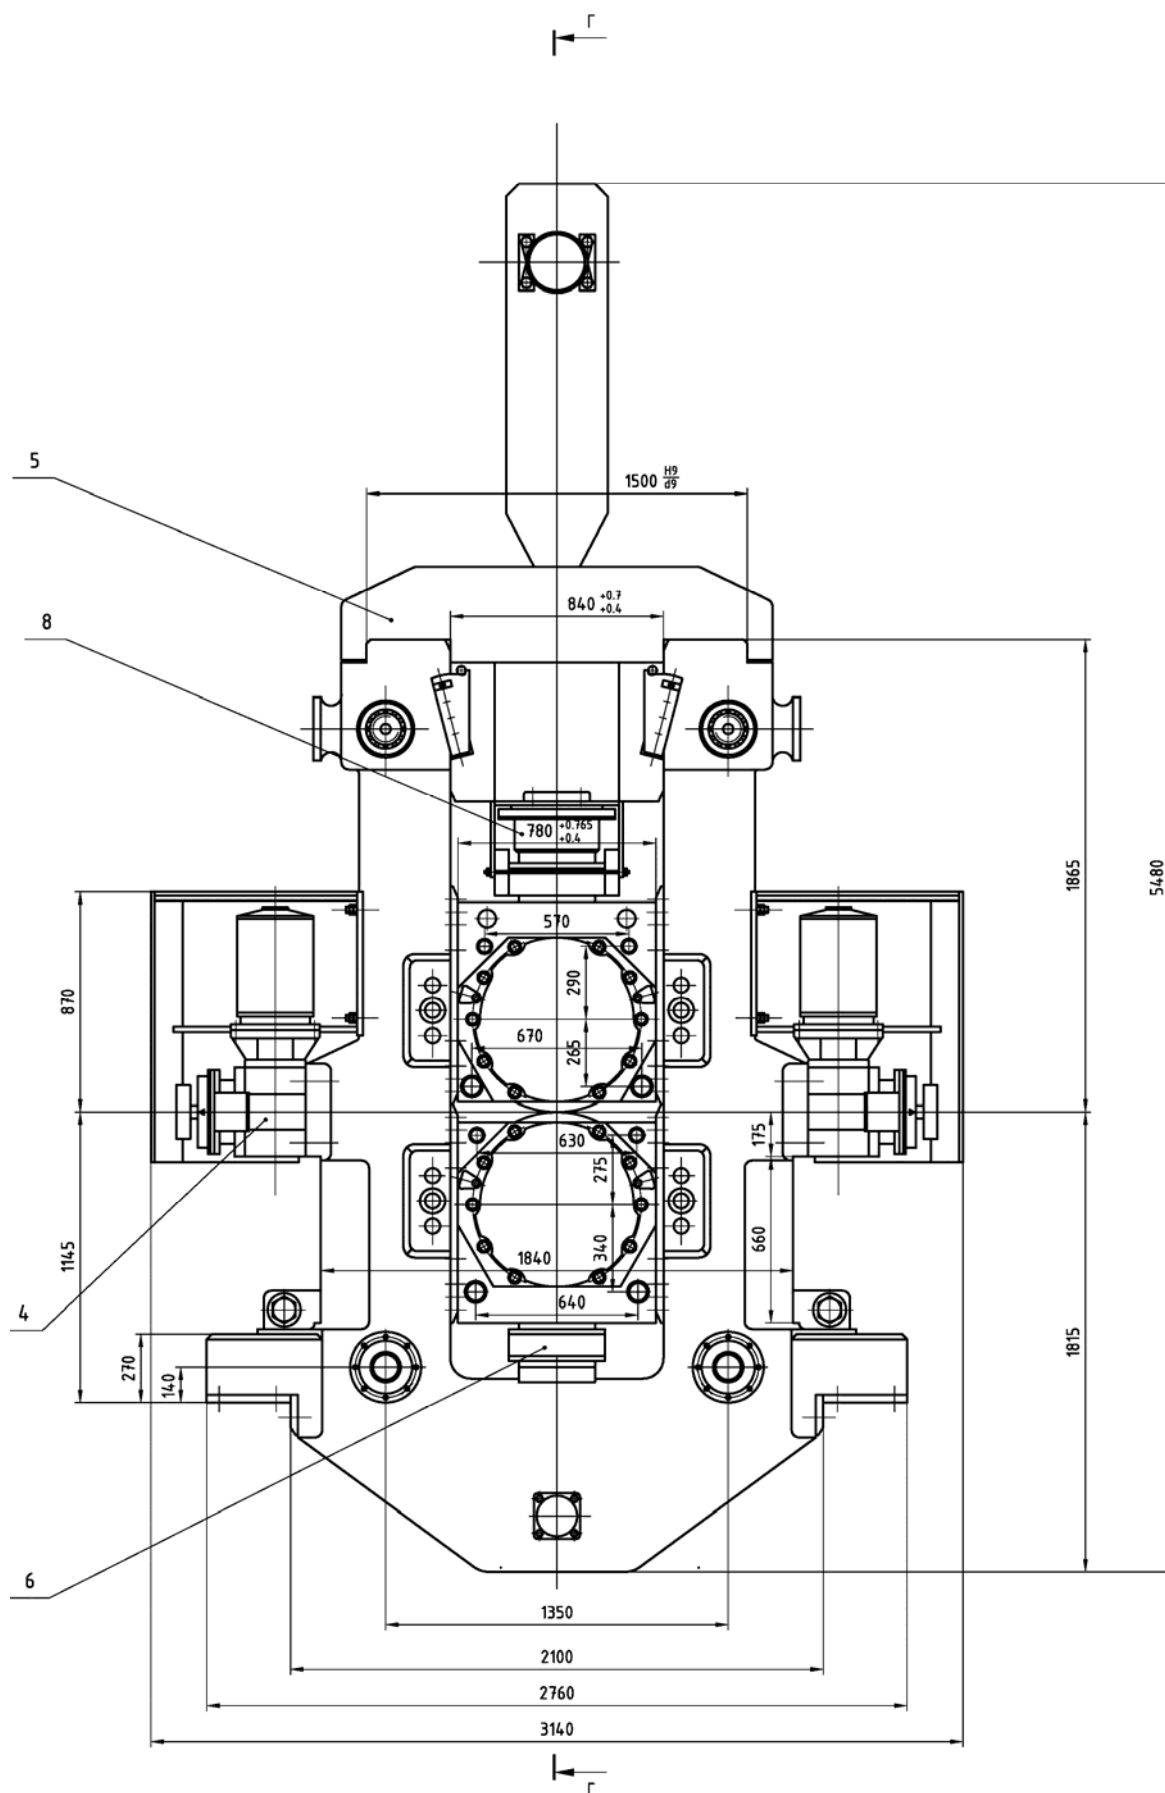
Кліть 730 ПН. Загальний вид (вид збоку)
